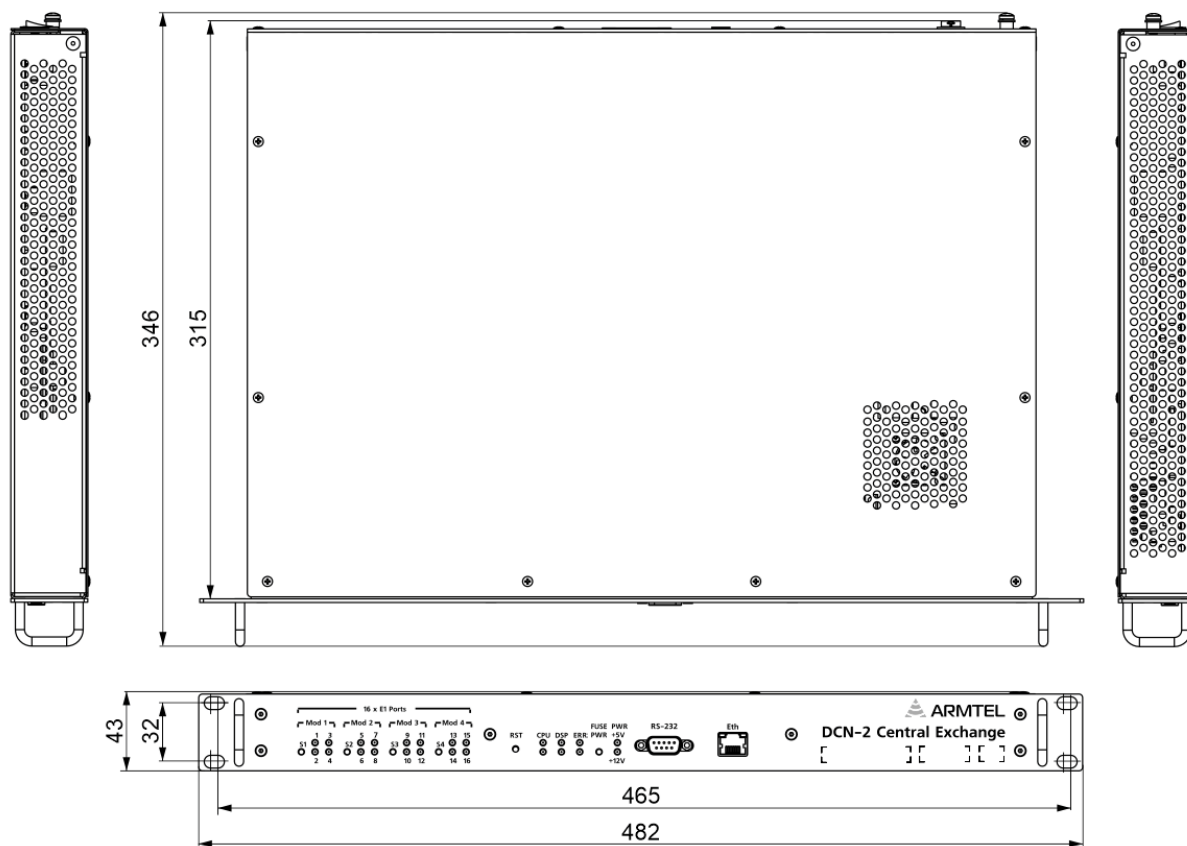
Внешний вид и габаритные размеры DCN-2
